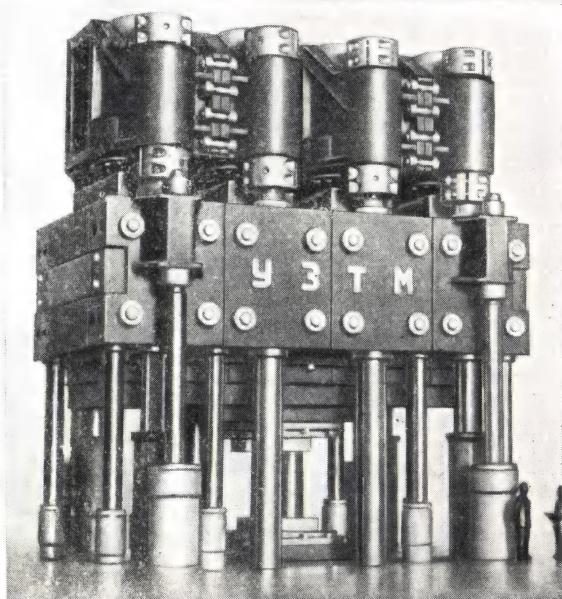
Гидравлический штамповочный пресс с усилием 30 000 т.
